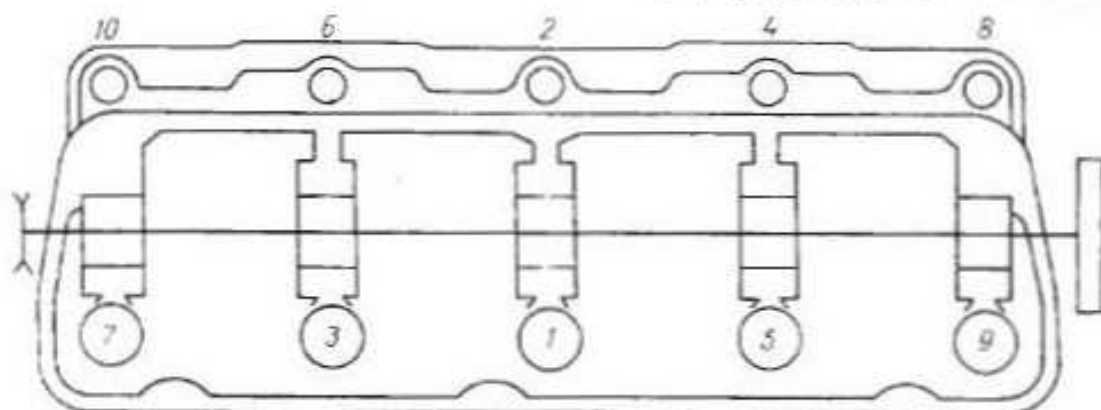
Порядок затяжки болтов крепления головки блока цилиндров.
